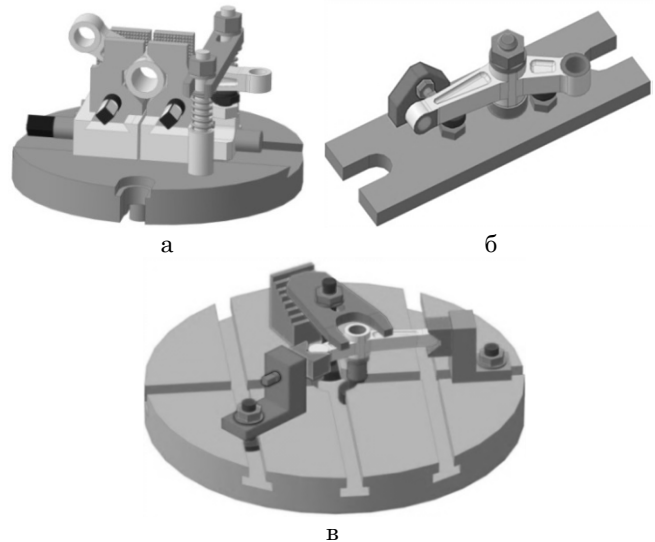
Верстатні пристрої для механічної обробки деталей типу важелів: а – на основі системи УЗПП; б – спеціальний; в – складений з елементів системи УЗП
